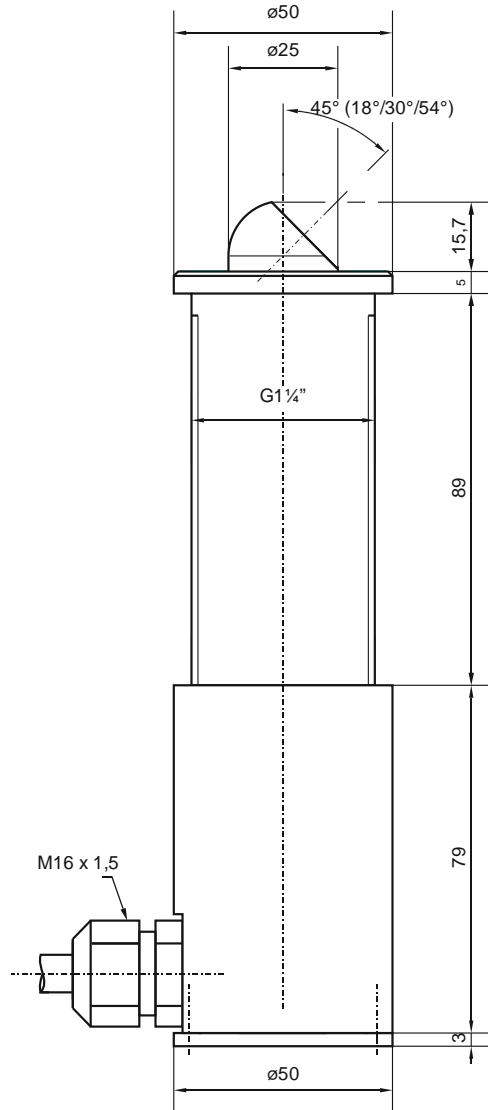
Maßzeichnung Einstecksensor Typ NOS-V2S
